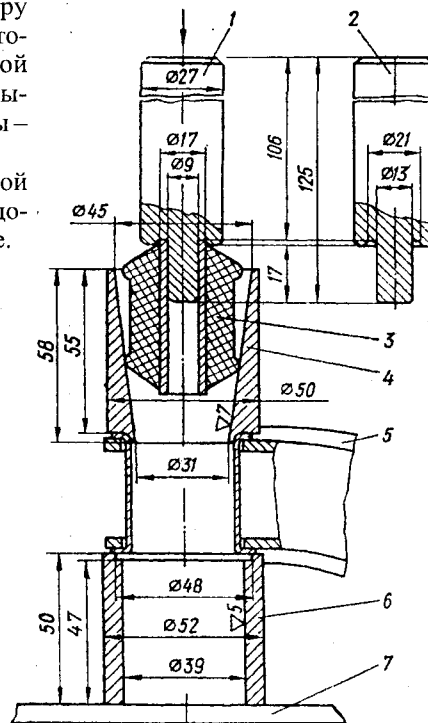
Запрессовка сайлентблока в гнездо рычага передней подвески: 1 – оправка запрессовки сайлентблока в рычаг; 2 – оправка для запрессовки сайлентблока в кронштейн реактивной штанги; 3 – сайлентблок рычага; 4 – стакан направляющий; 5 – рычаг; 6 – подставка; 7 – основание
